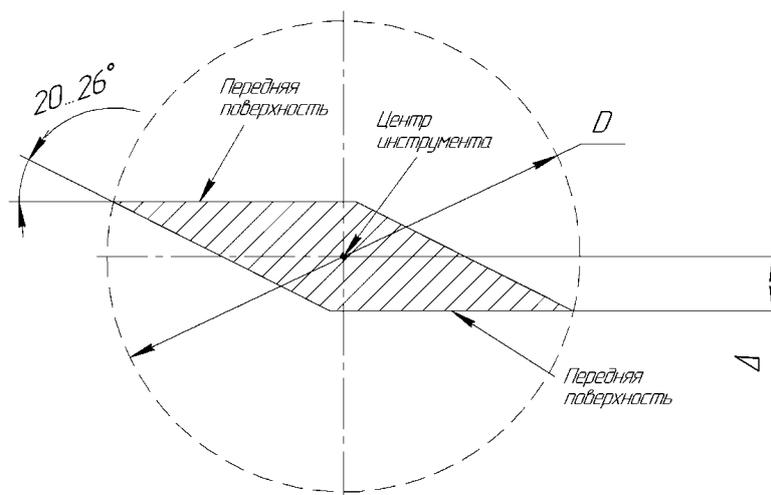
Сечение теоретического осевого инструмента для обработки отверстий типа TORX
